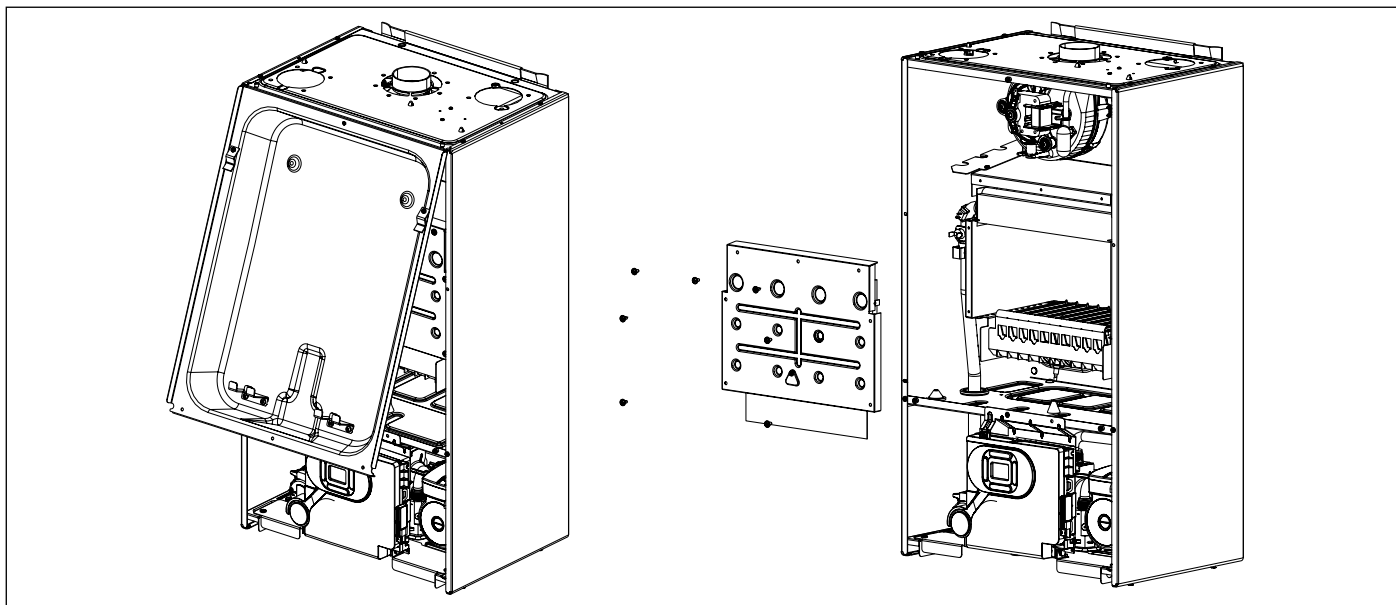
Demontaža nosača za zaključavanje ekspanzijske posude
